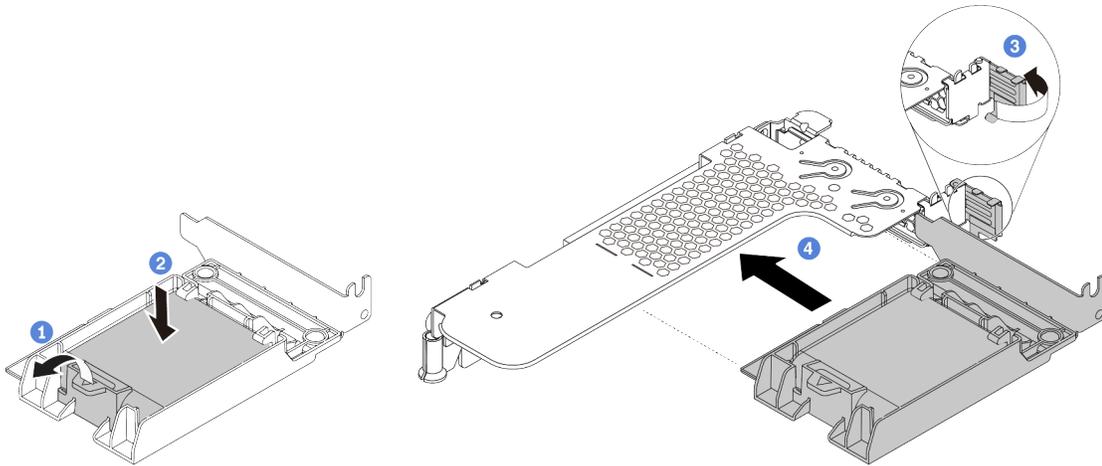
Installazione del modulo di alimentazione flash RAID sulla scheda verticale
